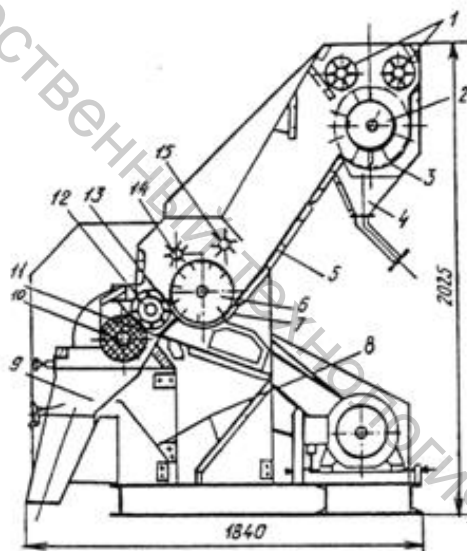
Схема валичного джина ДВ-1М: 1 – питающие лопастные валики; 2 – колковый барабан; 3 – перфорированная сетка; 4 – соровыводящий лоток; 5 – лоток; 6 – игольчатый барабан; 7 – колосниковая решетка; 8 – лоток; 9 – лоток; 10 – рабочий барабан; 11 – неподвижный нож с декой; 12 – отбойный барабан; 13 – перфорированная сетка; 14 – ускоряющий валик; 15 – разравнивающий валик
